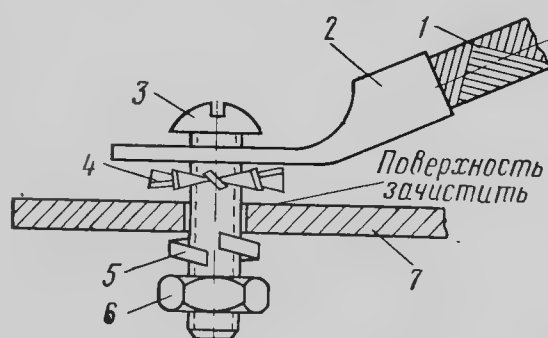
Типовое крепление перемычки металлизации с помощью болта и гайки:
